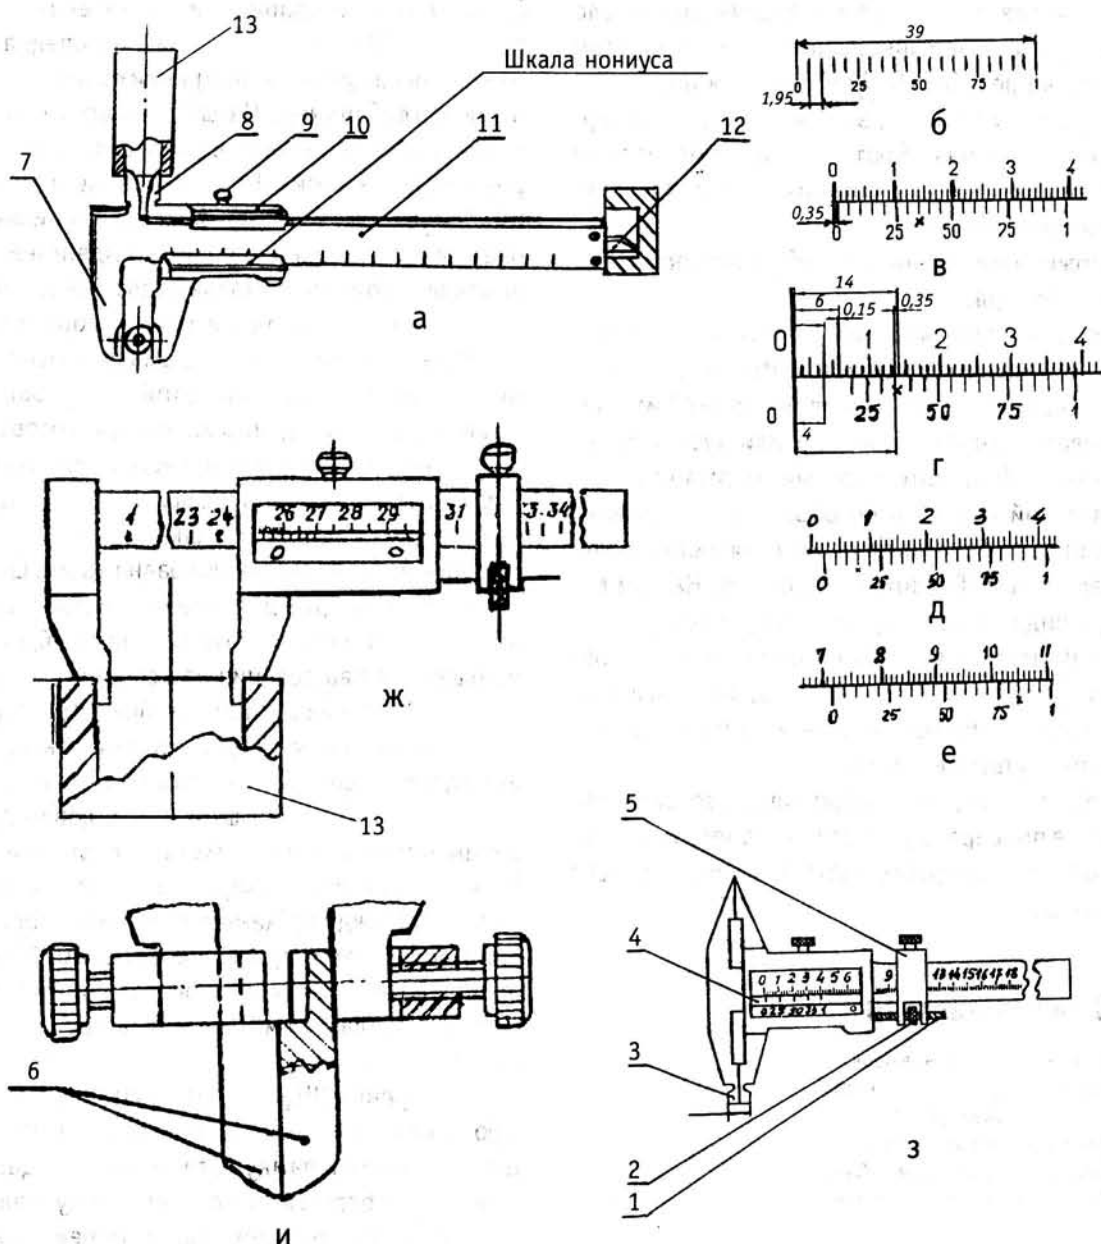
Штангенциркули: а — ШЦ-1; б — шкала нониуса с величиной отсчета 0,05; в — совпадение 7-го штриха нониуса со штрихом на шкале штанги; г, д, е — примеры отсчета; ж — ШЦ-Ш; з — ШЦ-11; и — приспособление для разметки к штангенциркулям ШЦ-11 и ШЦ-Ш; 1 — винт микрометрической подачи; 2 — гайка микрометрической подачи; 3 — утолщенная неподвижная губка; 4 — пластина нониуса; 5 — рамка микрометрической подачи; 6 — резцы; 7 — неподвижная длинная губка; 8 — подвижная губка; 9 — винт; 10 — рамка с нониусом; 11 — штанга; 12 — глубиномер; 13 — измеряемая деталь
